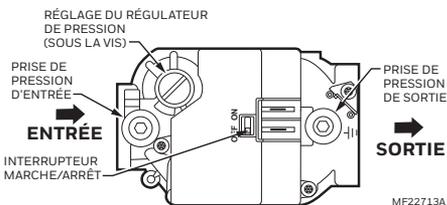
Vue de haut des régulateurs à gaz combinés VR8205S, T.
